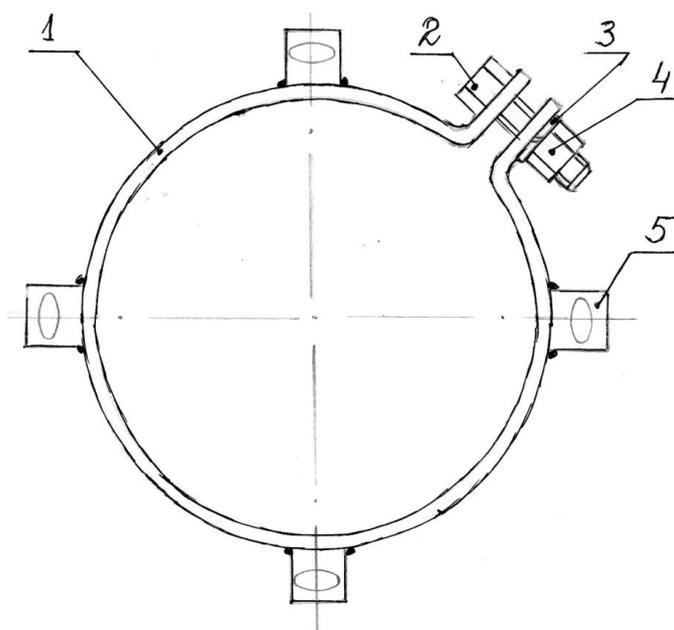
Конструкция для крепления средств защиты, работающих на длинномерных высотных опорах (вид сверху)
